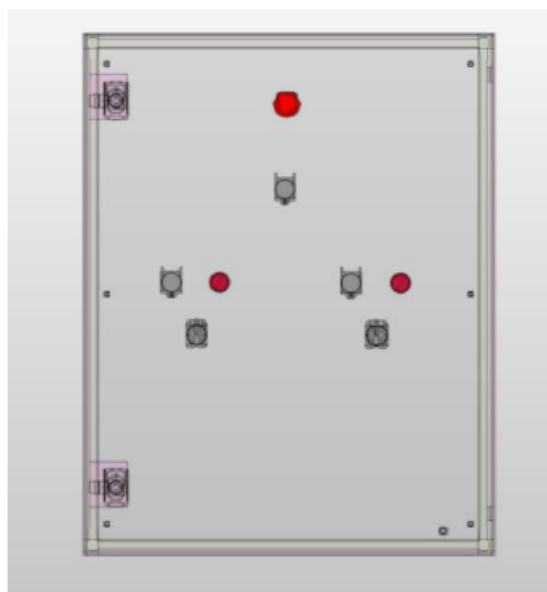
Vista frontal del tablero, diseñado en EPLAN
